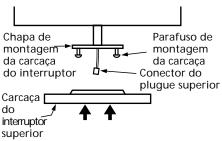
Fixando a carcaça do interruptor superior à chapa de montagem da carcaça do interruptor
